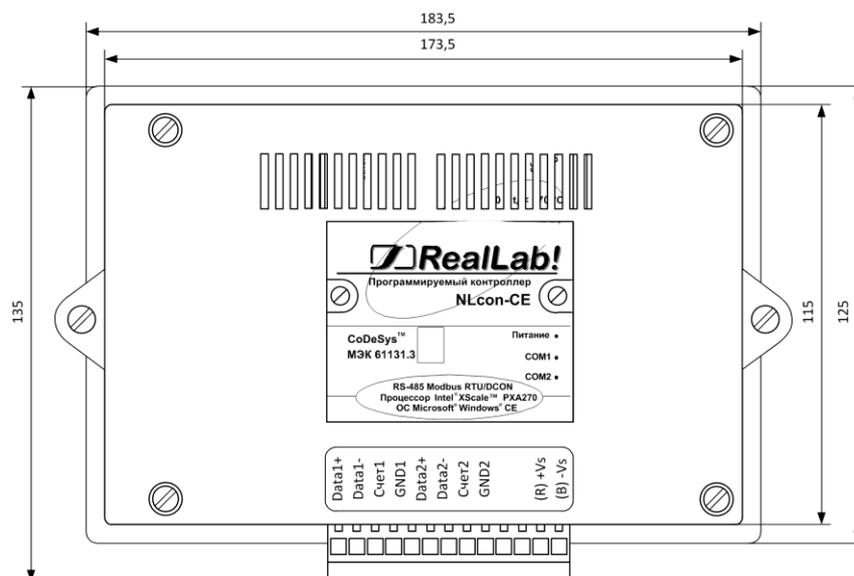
Габаритный чертеж ПЛК, вид сзади
